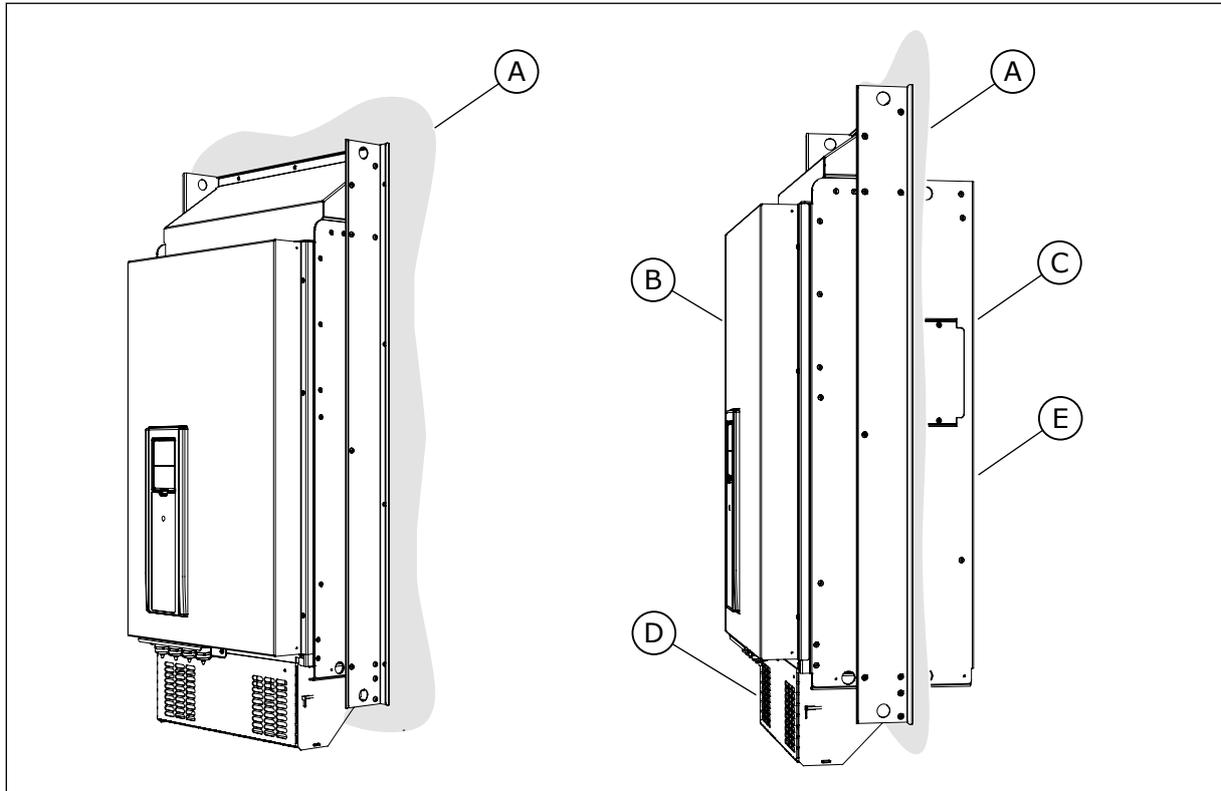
Beispiel für die Flanschbefestigung (Baugröße MR9)
